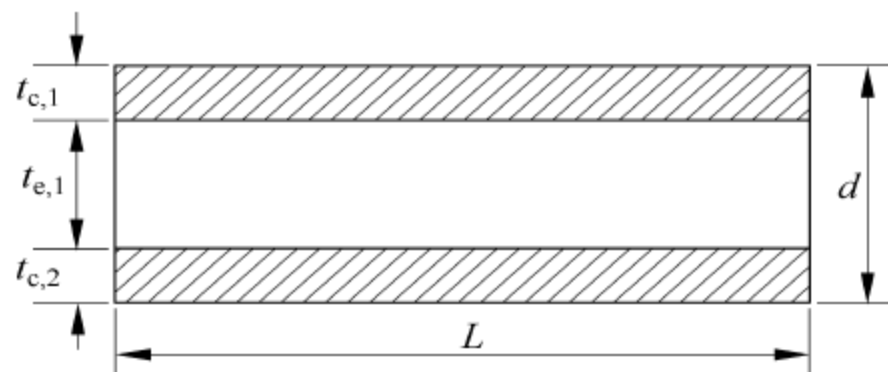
双层覆铜 PCB 板结构示意图及尺寸参数
